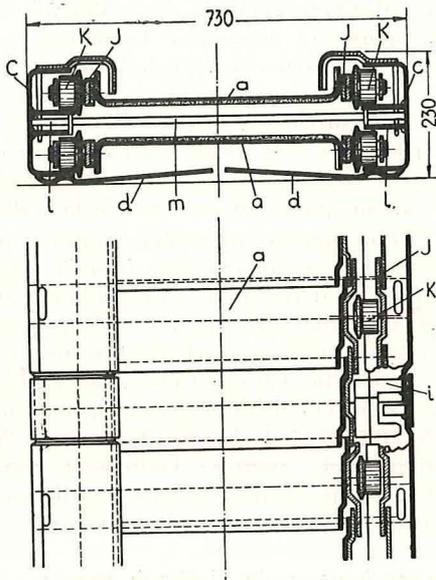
Coupe en travers et vue en plan du convoyeur Erbö.
